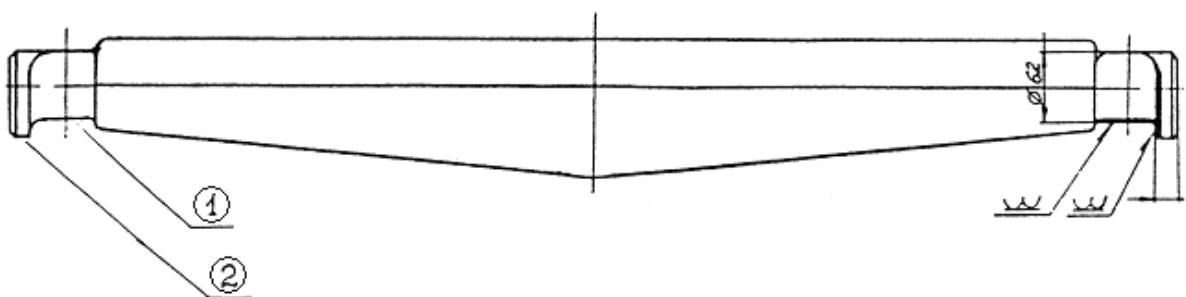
Изношенные поверхности опорной балки тележки вагона ЦМВ
